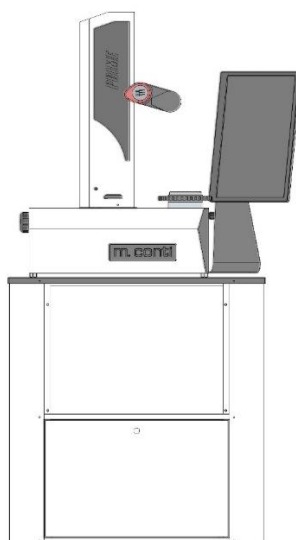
Эскиз прибора размерной настройки инструмента M.CONTI PRIME
